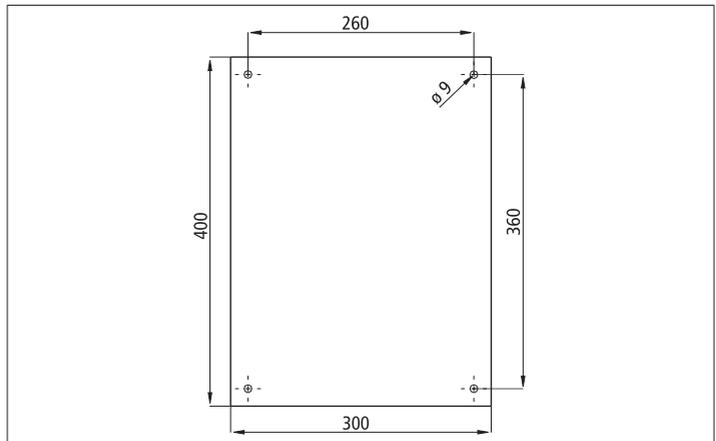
Rückansicht SVG 522 ohne Befestigungslaschen
